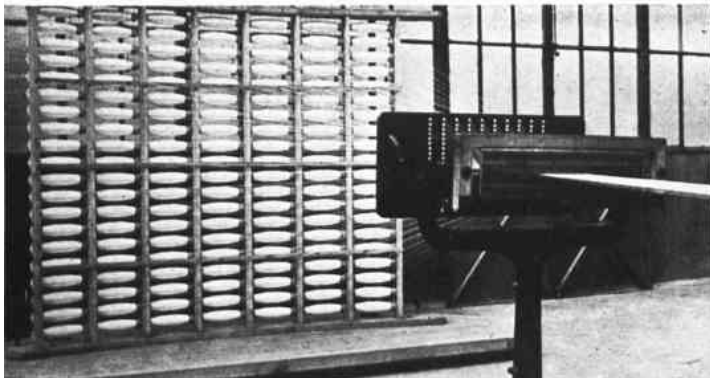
Cantre à la déroulée. Vue d'ensemble.
